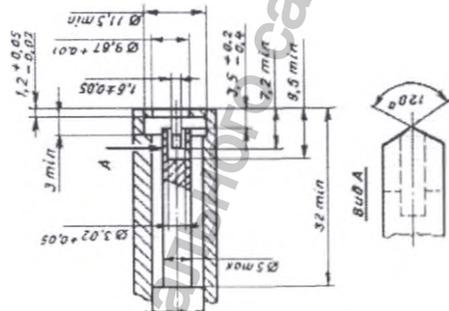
Конструкция, размеры и допуски присоединительной части наконечника (задней части)
